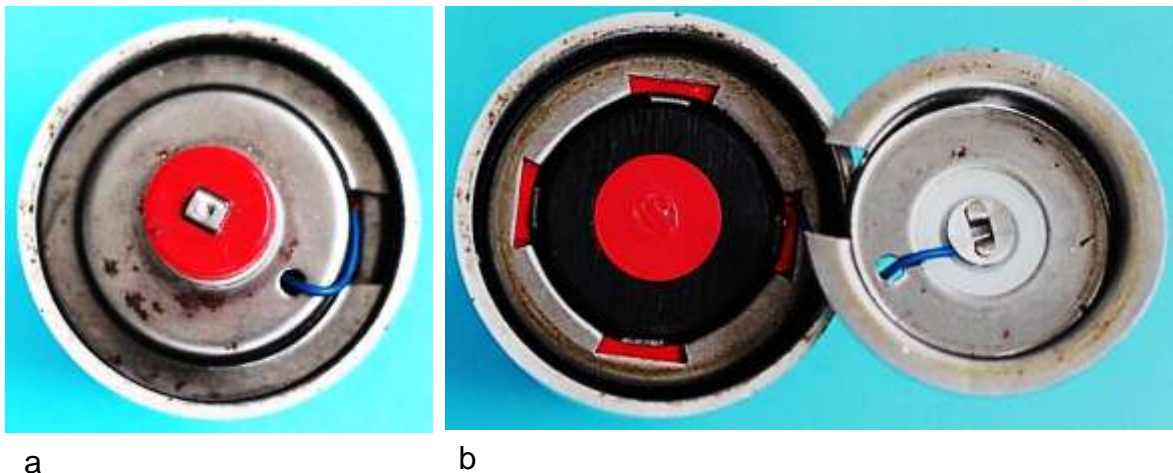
Aluminiumgehäuse: a) Lagerhals, b) Bodenansicht
